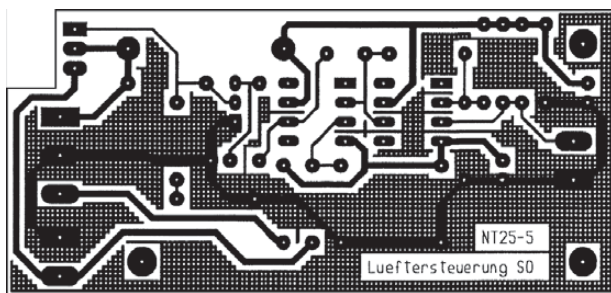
Layout der Lüftersteuerung; Abmessungen: 80,5 × 37,5 mm², M 1:1
